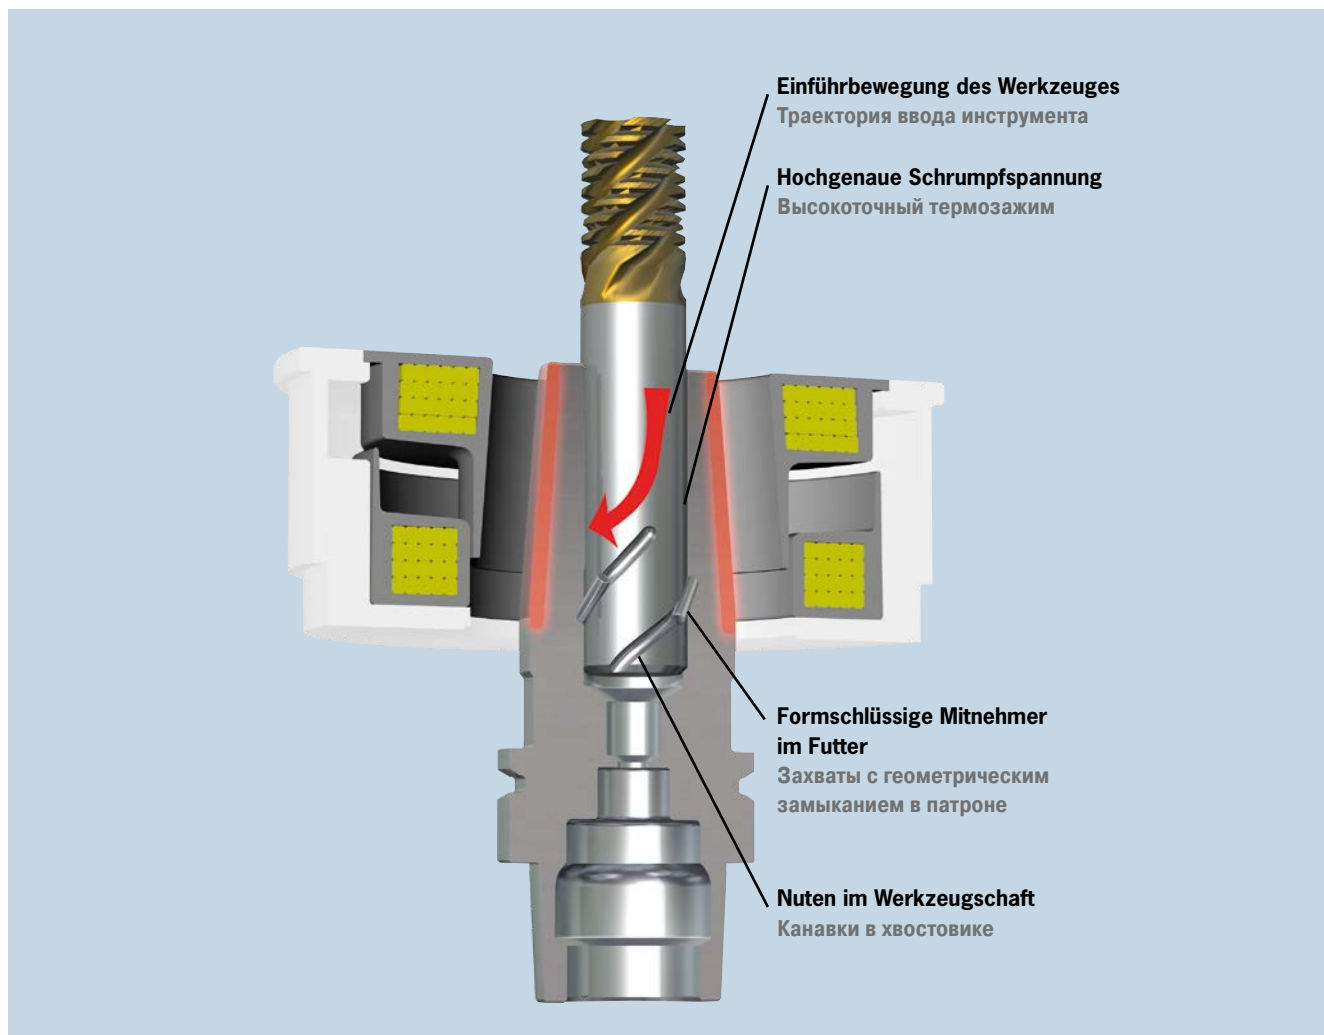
Mit Safe-Lock™ kein Werkzeugauszug
